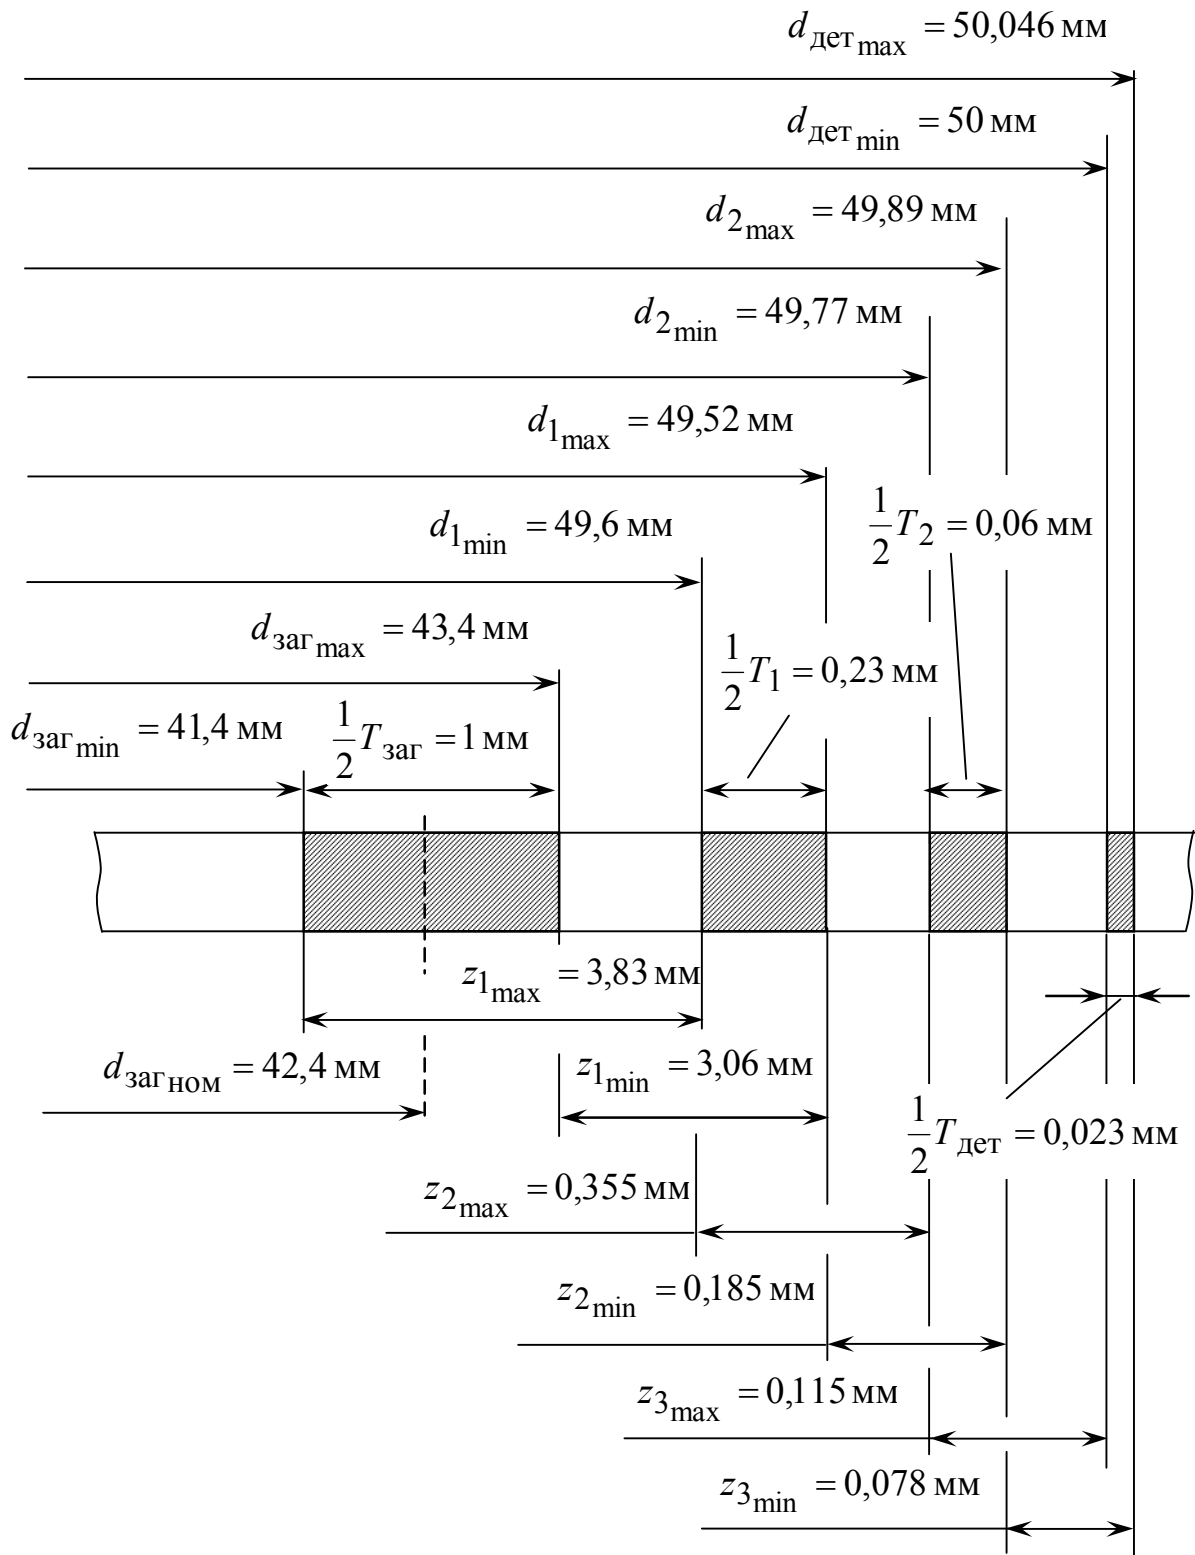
Схема розташування розмірів, припусків і допусків на обробку отвору в корпусі підшипника
